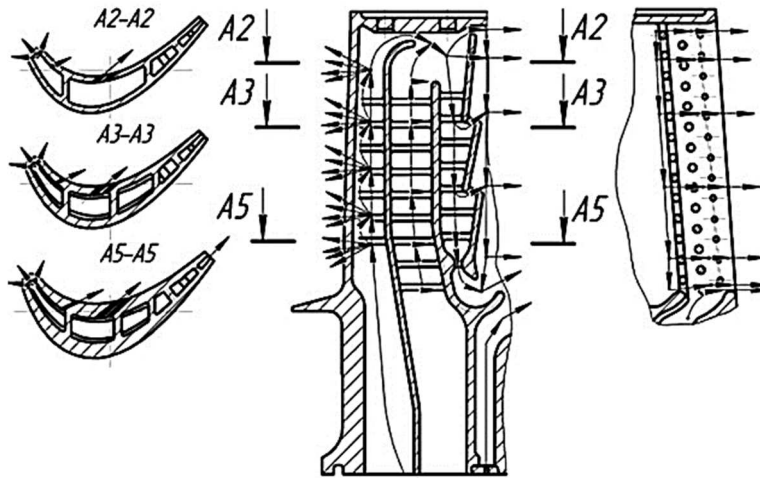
Конструктивная схема лопатки рабочего колеса ТВД с плёночным охлаждением
